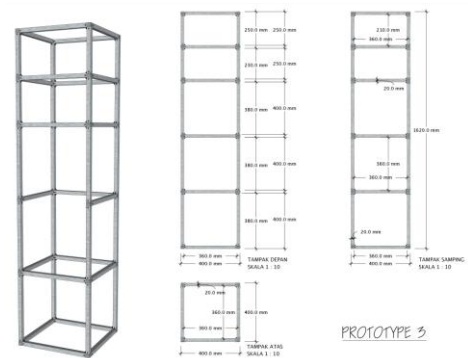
Konstruksi, Detail dan Assembly Modul
